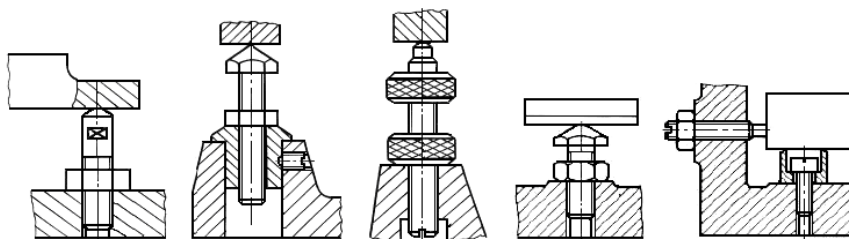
Установка заготовок на регулируемые винтовые опоры
